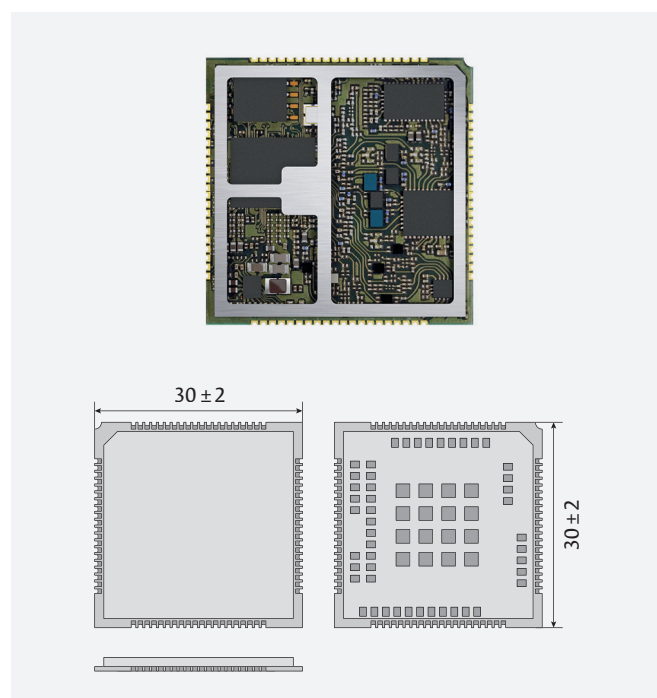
Внешний вид и размеры модуля ПР1803Н
